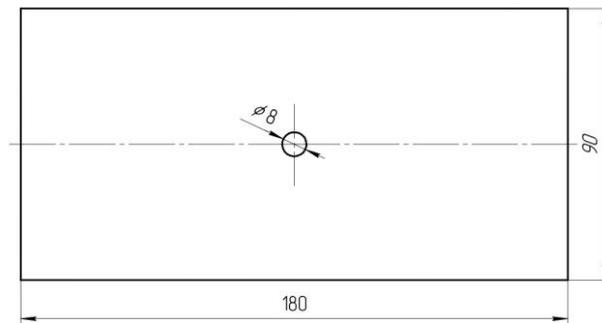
Фронтальное изображение корпуса приспособления для полировки
